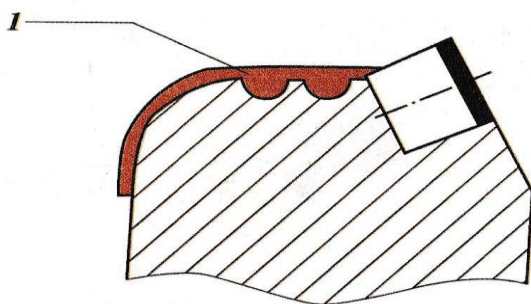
Конструкция усиленной наплавки на лопастях долота
